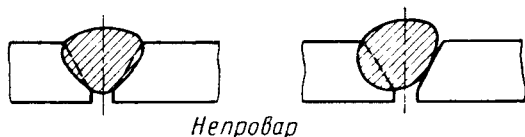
Дефекты сварки при недостаточном разогреве
